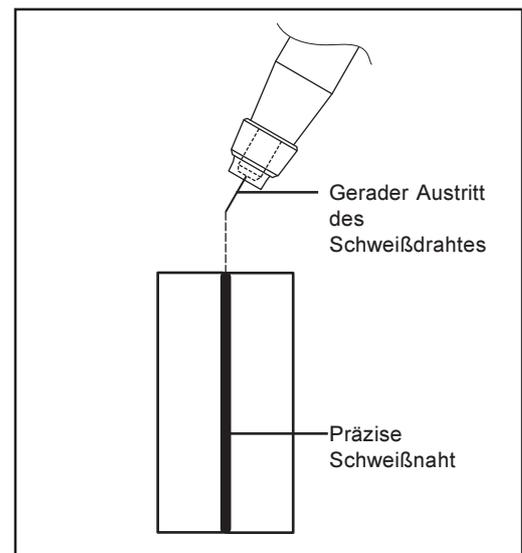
Exakte Schweißnaht bei Drahttrichtung
